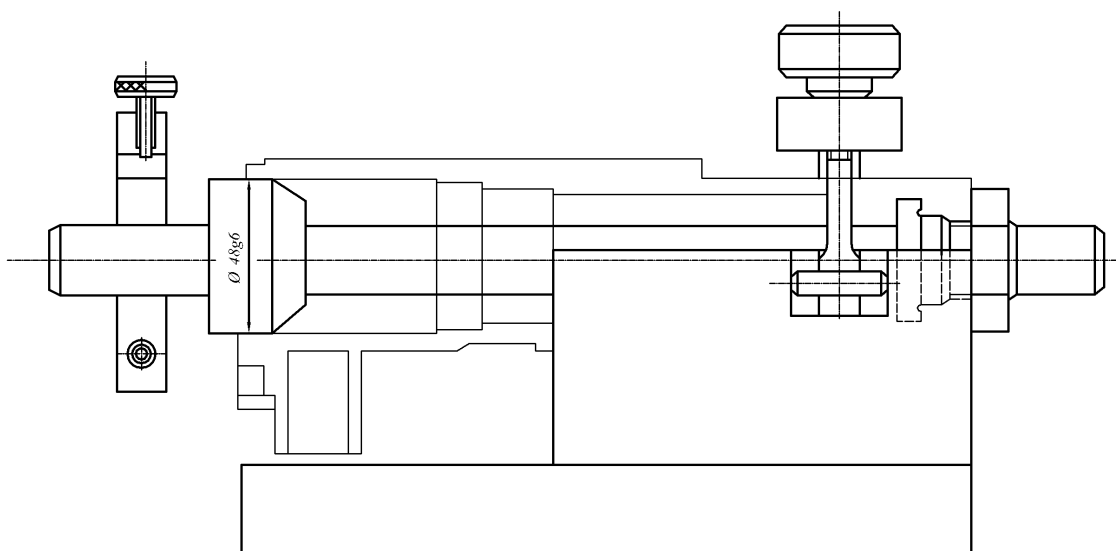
Пристрій для контролю торцевого биття та паралельності поверхонь корпусу
